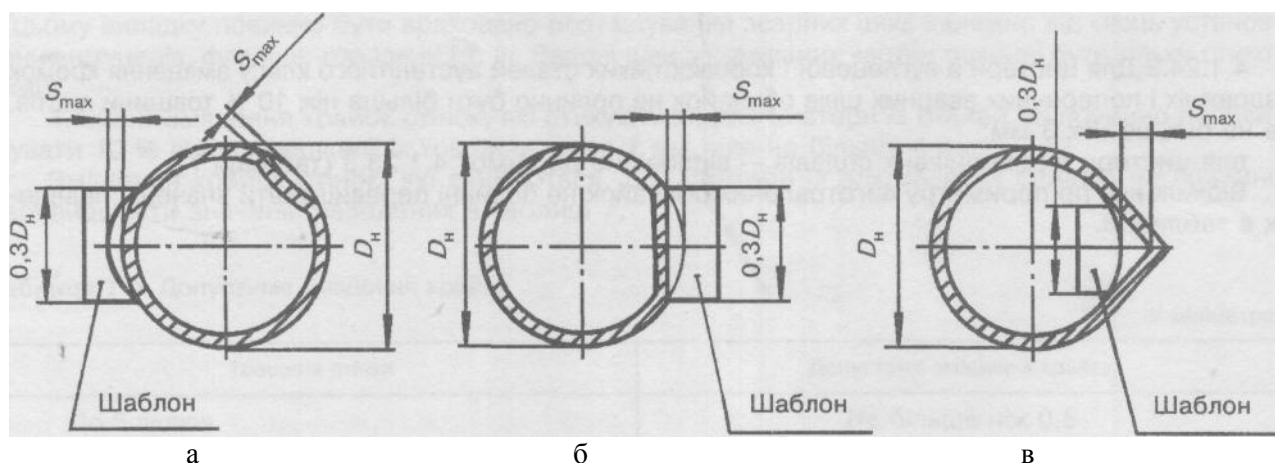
Види і допуски відхилень від геометричної форми обичайки
